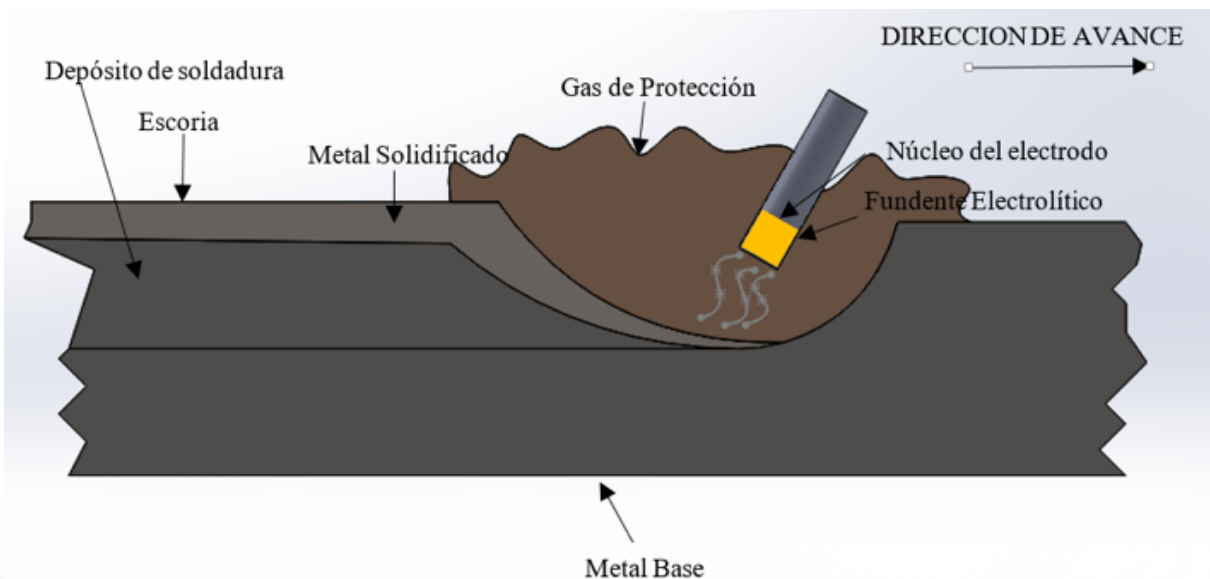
Esquema del arco eléctrico empleado en soldadura manual
